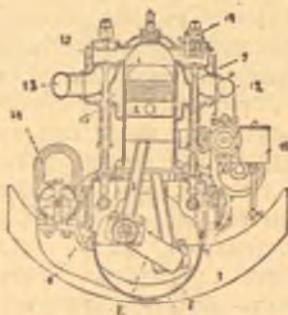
Бензиновый двигатель. Поперечный разрѣзъ.
